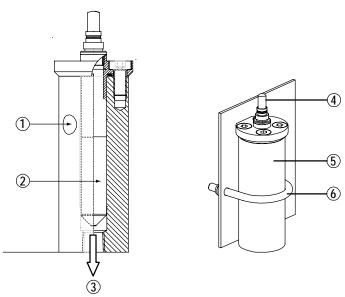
Дополнительная колба для образцов HMP 302 SC
